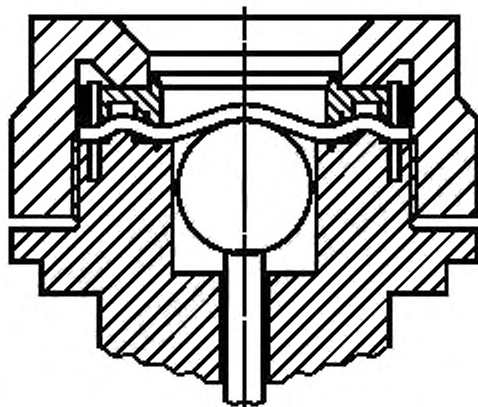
Сечение зажимной головки с установленным образцом для испытаний
